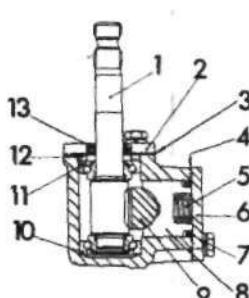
Поперечное сечение зубчатой рейки у шестерни и демпферного крепления (Раздел 6)
